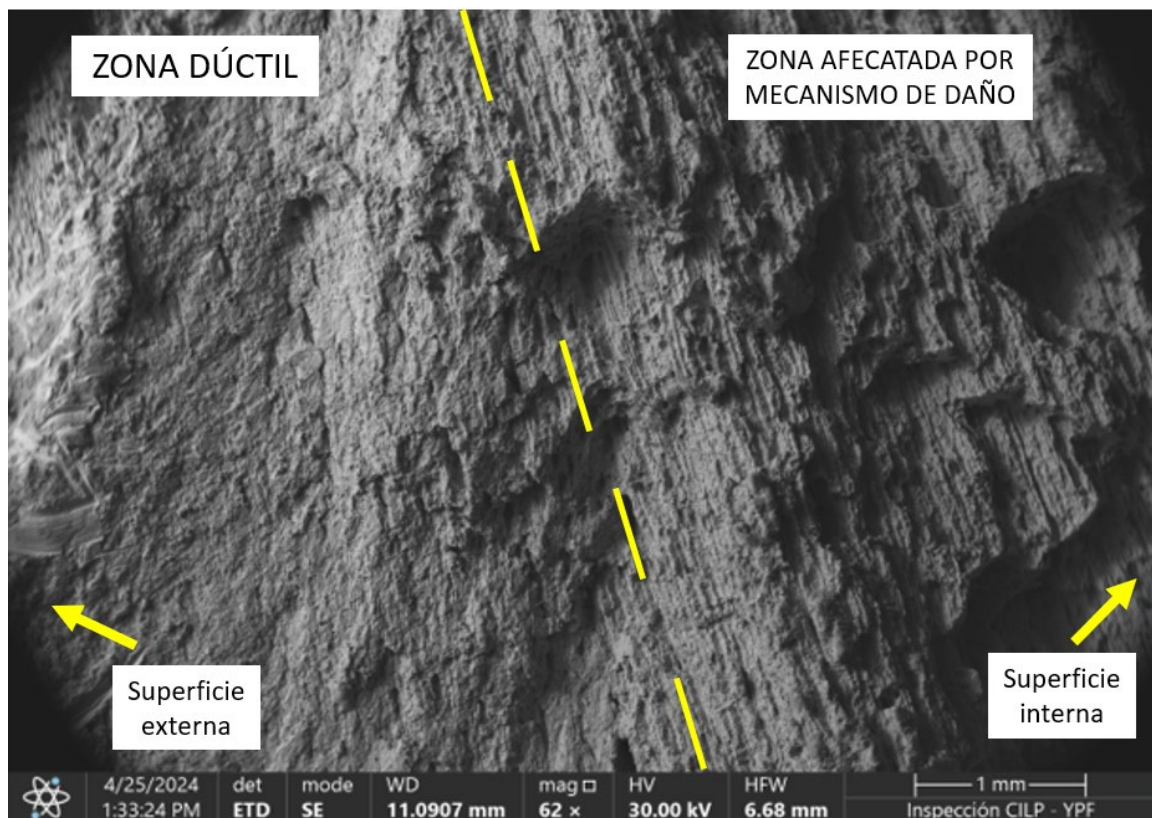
Superficie de fractura línea de fusión / ZAC – Codo inferior – Cordón longitudinal. Se identificó una zona dúctil y otra zona con daño que cambia aproximadamente en la mitad del espesor.
